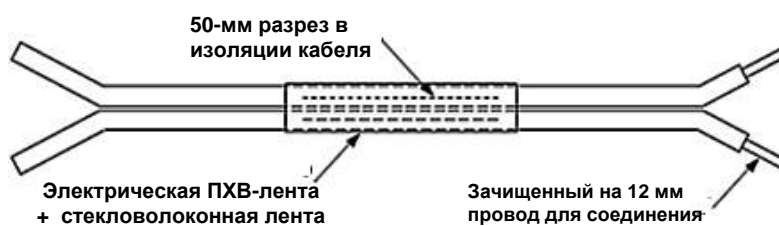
Подготовка образцов кабеля (9.9.2.6)
